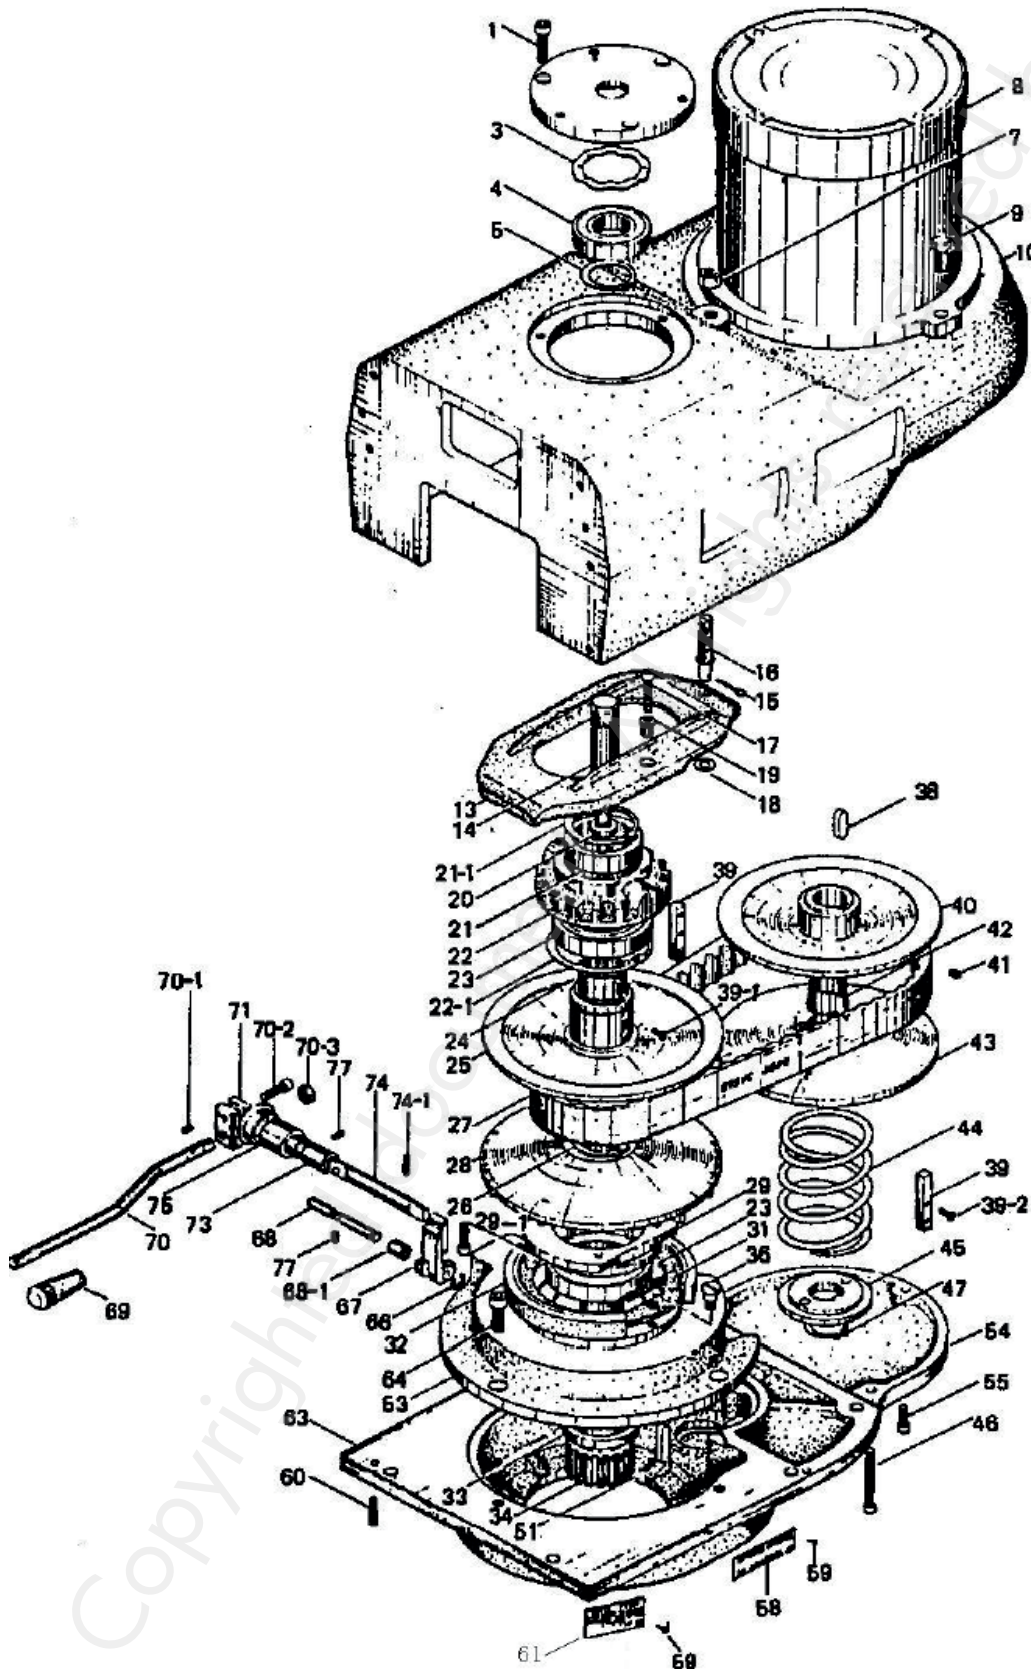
Boîte de vitesse de la tête de fraiseuse - Partie B
